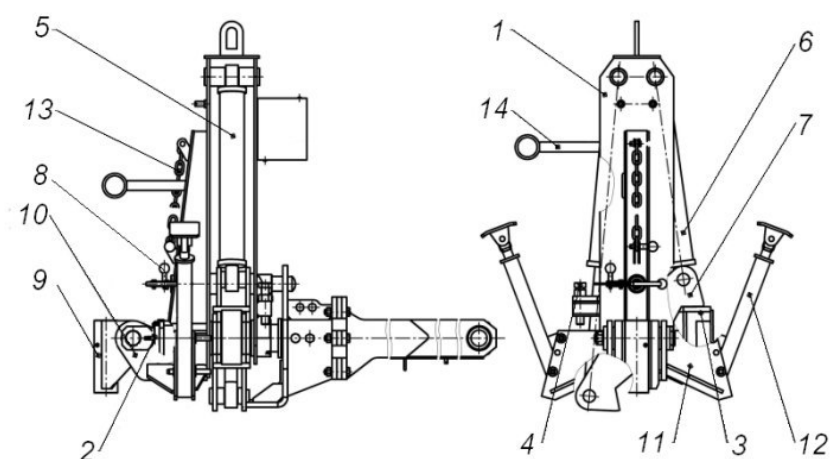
Механизм оборота рамы: 1 – корпус; 2 – вал шлицевой с фланцем; 3 – упор; 4 – болт регулировочный; 5, 6 – гидроцилиндры; 7 – рычаг; 8 – фиксатор; 9 – крестовина; 10 – понизитель корпуса; 11, 14 – кронштейны; 12 – опора; 13 – цепь
